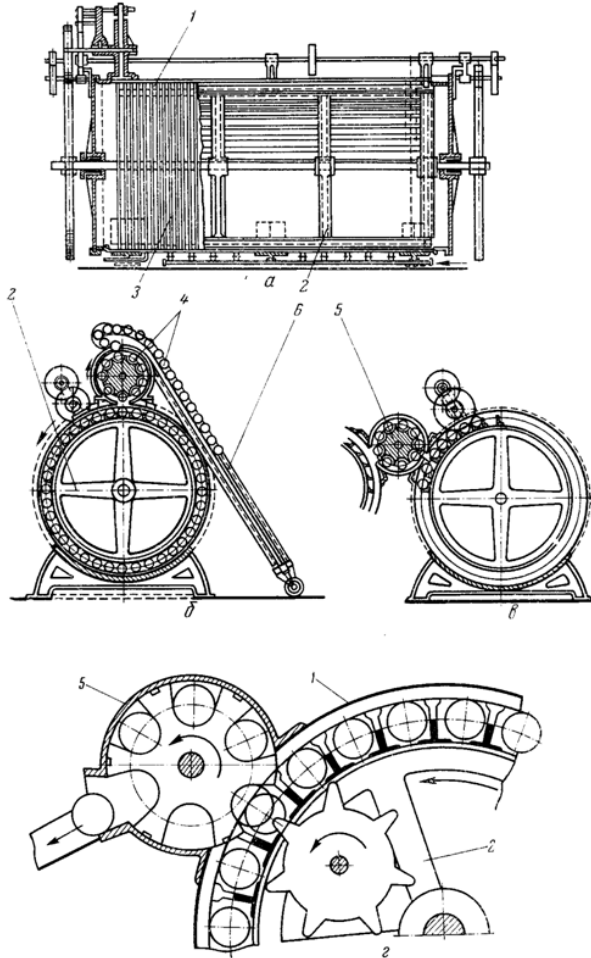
Роторний стерилізатор безперервної дії: а – загальний вигляд; б – завантажувальний клапан; в, г – розвантажувальний клапан; 1 – корпус; 2 – ротор; 3 – спіралеподібна напрямна; 4 – завантажувальний клапан; 5 – розвантажувальний клапан; 6 – ланцюговий елеватор-живильник.
